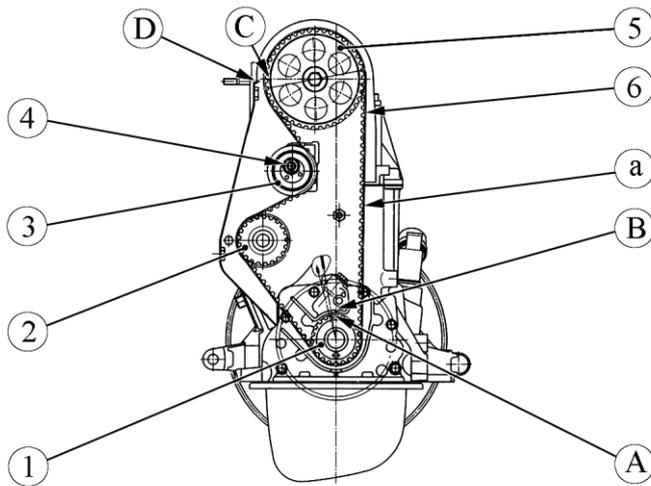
Детали привода распределительного вала двигателя 11183:
